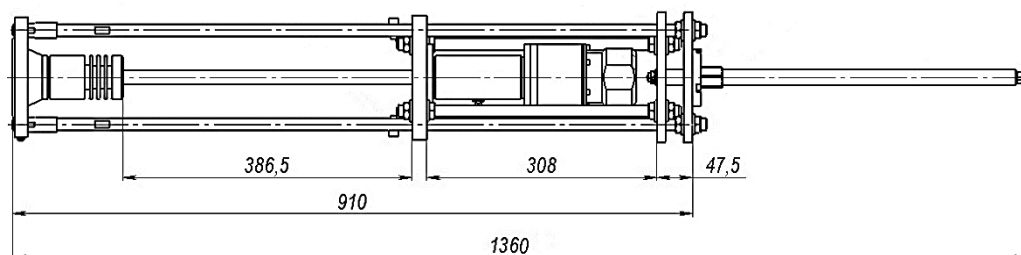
Габаритные размеры приемопередатчика КТМ100 ФЛ ЛБ (с установочным приспособлением)
